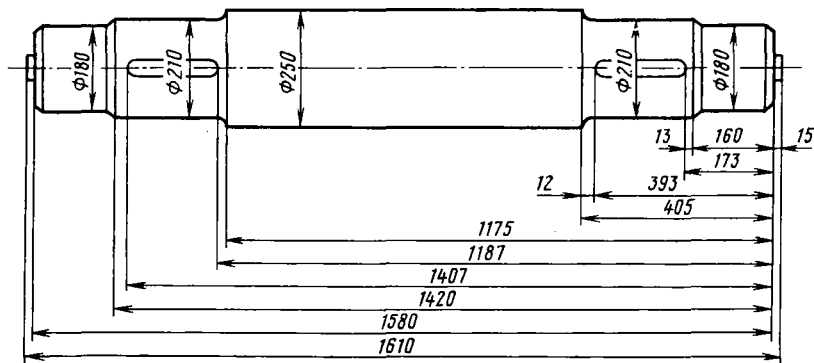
Главный приводной вал эскалатора ЛТ-4
